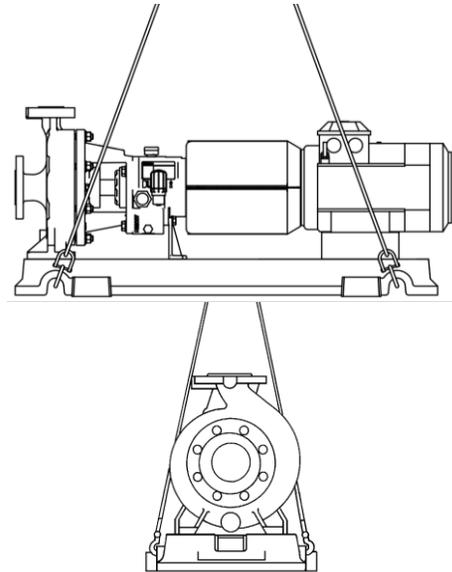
Içamento da bomba com conjunto de placa de base de ferro fundido ou aço fabricado
